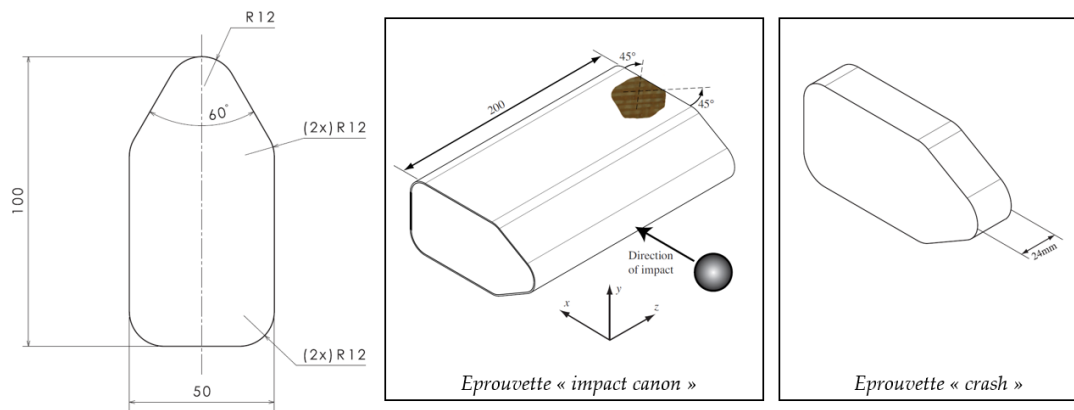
Géométrie des éprouvettes d'impact et de crash.
